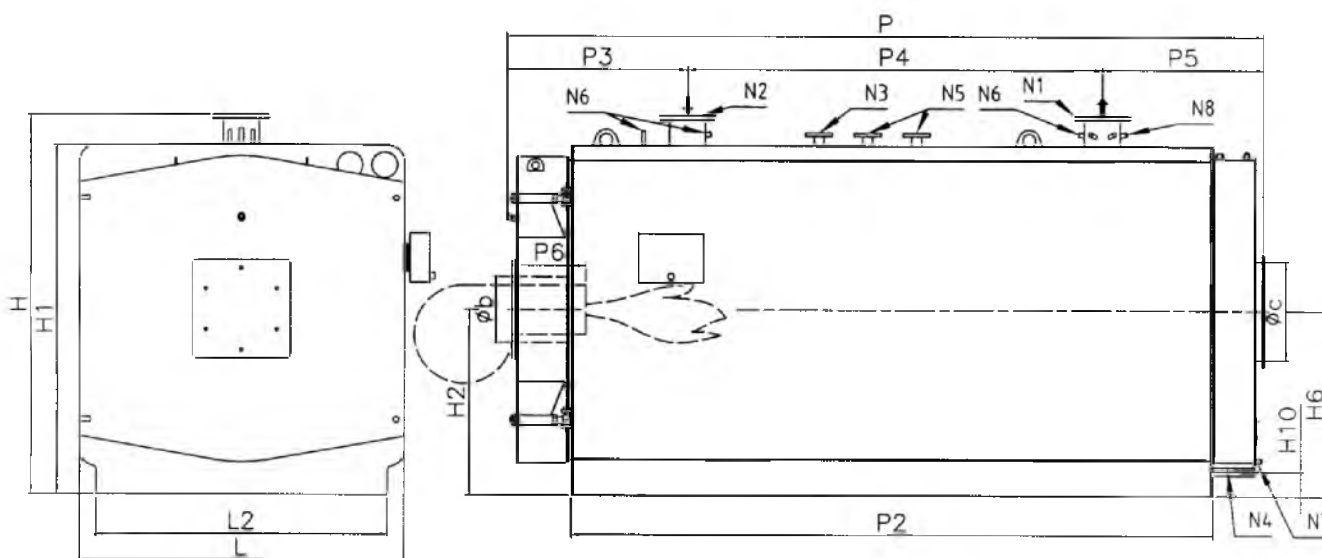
Устройство котла Ici Caldaie REX-3000
